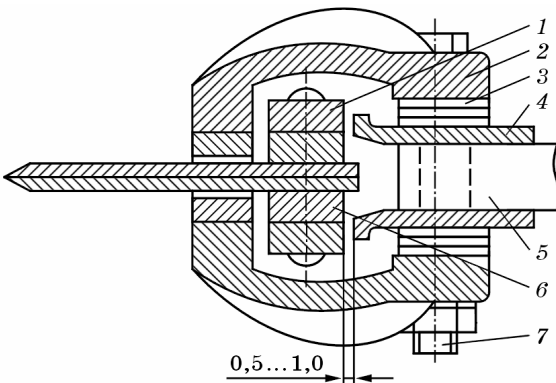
Різальний апарат з двома рухомими ножами:
